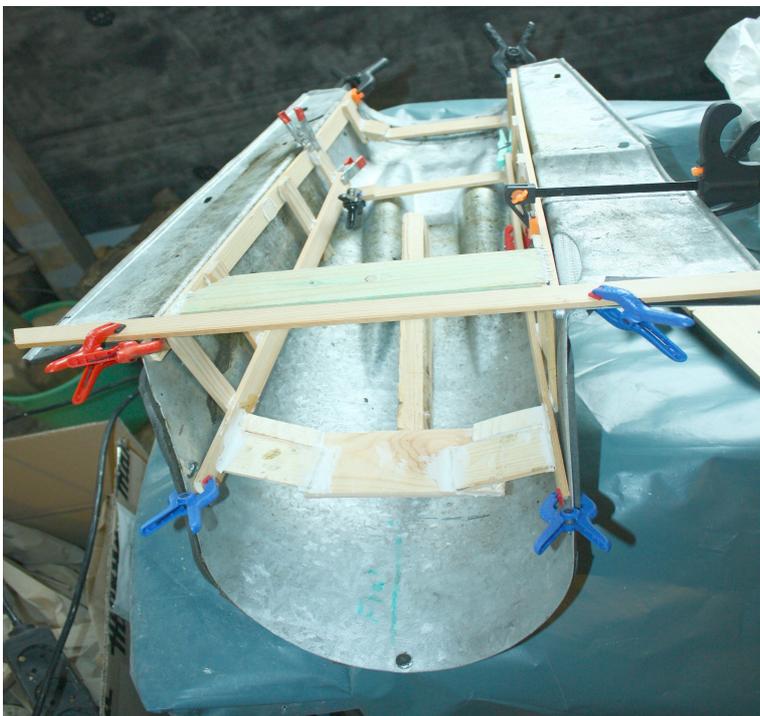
Gerippe-Bau, angepasst an den Sb-Getriebetunnel
